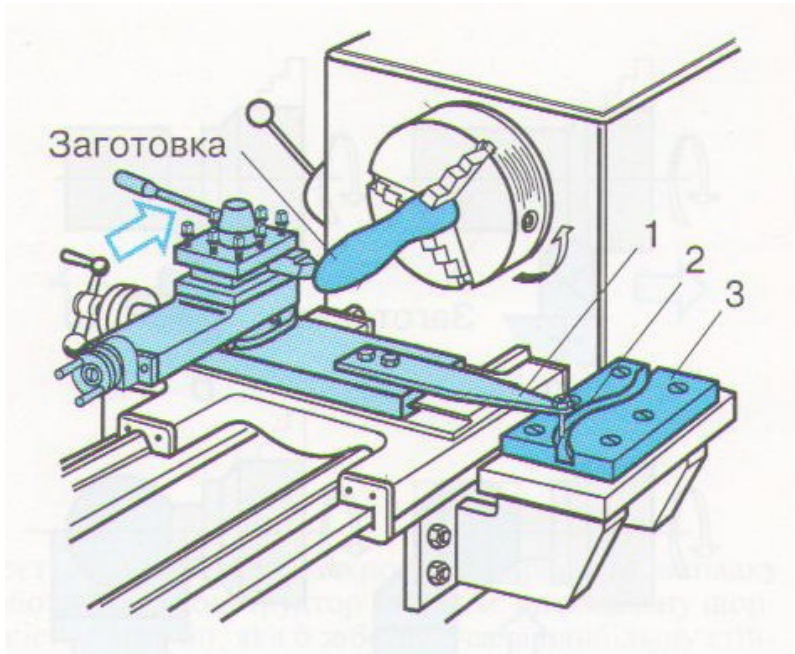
Обробка фасонної поверхні за допомогою копіювального пристрою:
